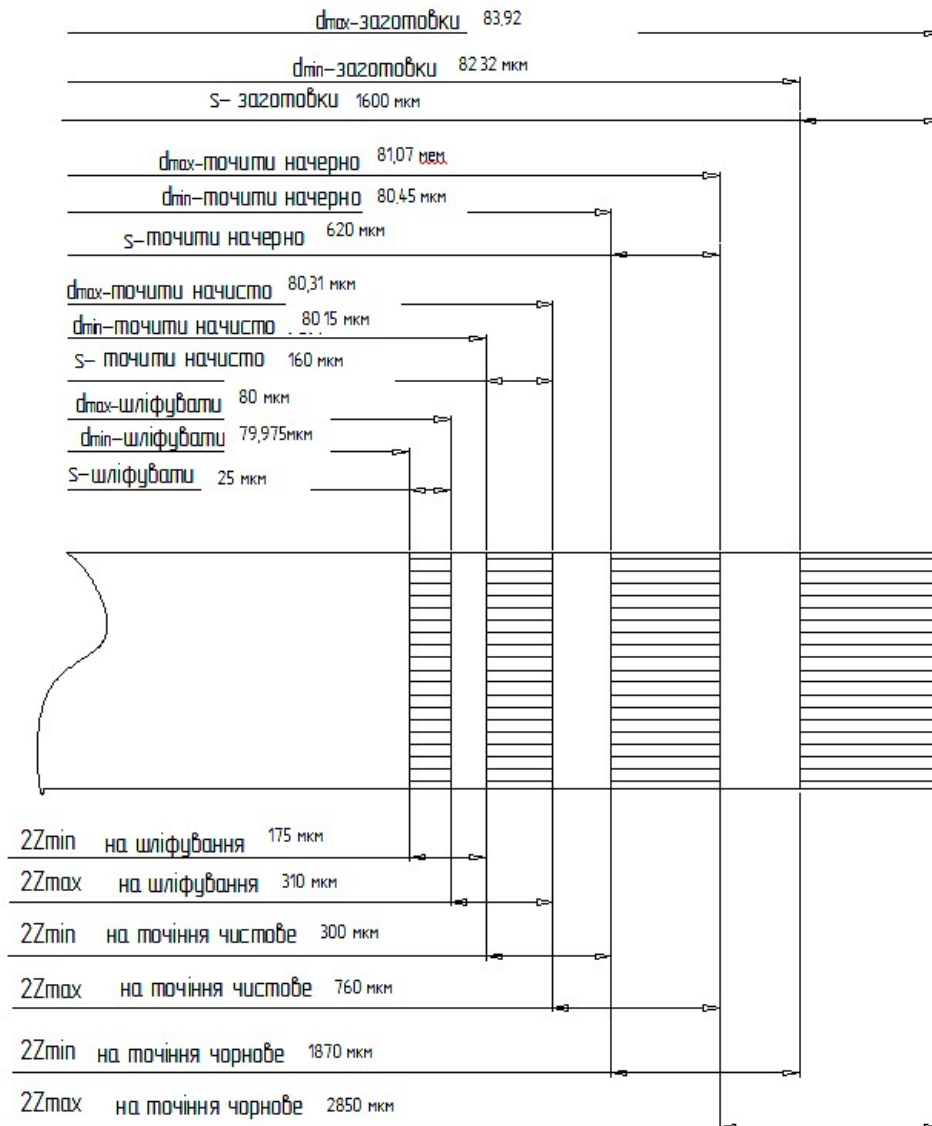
Схема розташування припусків та допусків на обробку поверхні
